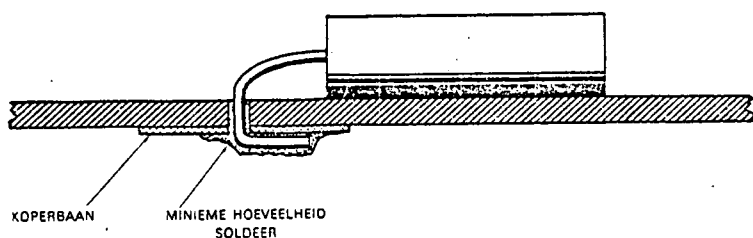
Voor soldeerverbindingen op prints is maar heel weinig soldeer nodig.
